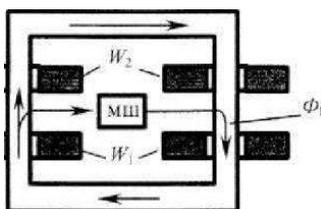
Устройство сварочного трансформатора с подвижным шунтом
